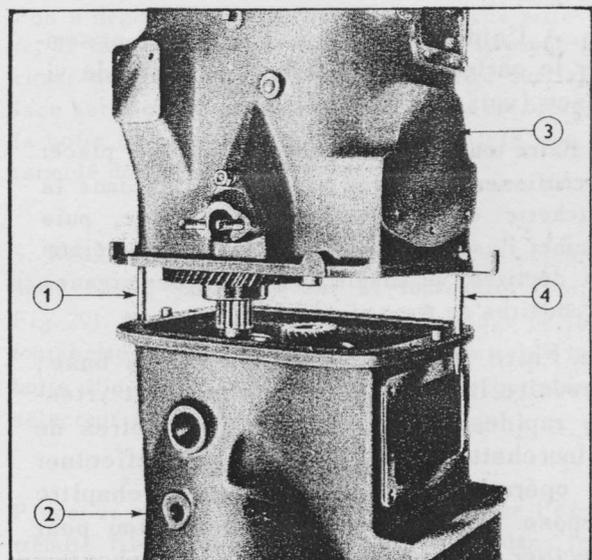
= Assemblage des Carters d'embrayage et de boîte de vitesses
